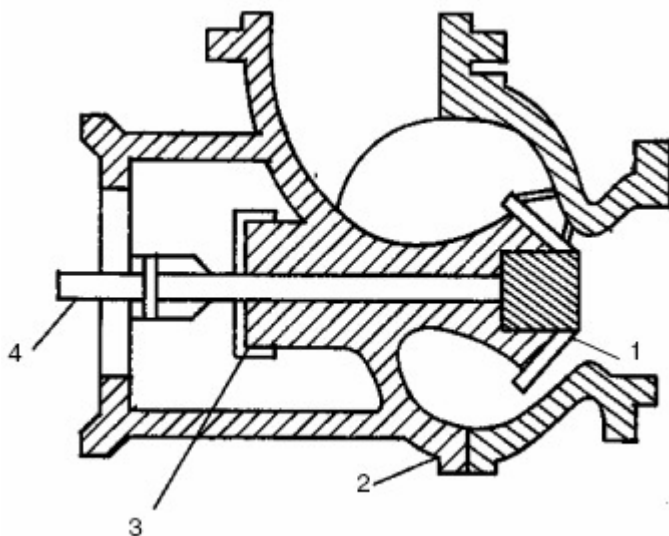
Циркуляционный насос ЦНИПС: 1 – колесо рабочее; 2 – корпус насоса; 3 – уплотнение-сальник; 4 – вал двигателя
